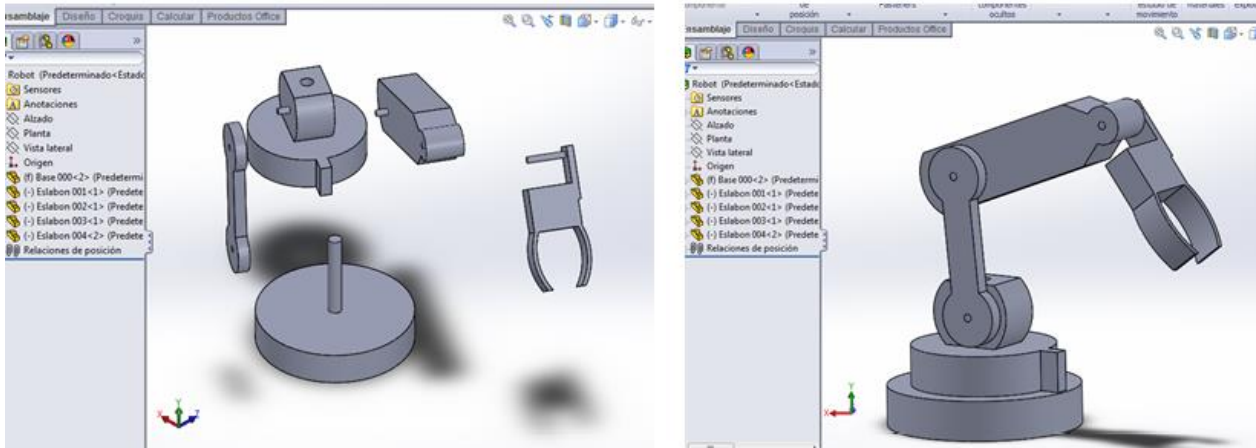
Izquierda: Piezas sin ensamblar, Derecha Robot ensamblado
